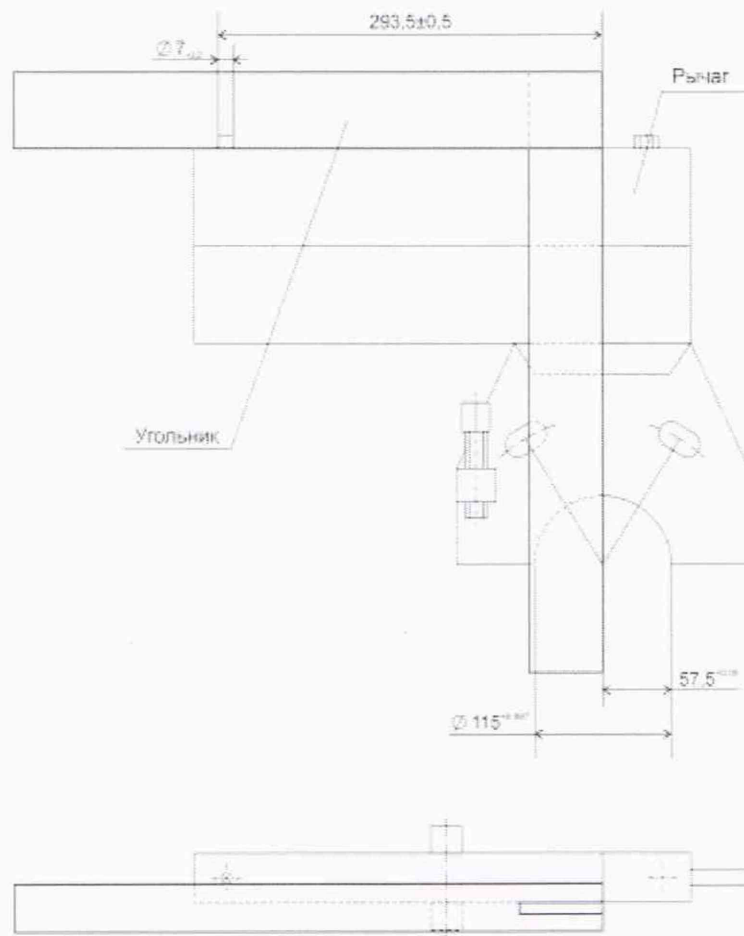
Чертеж рычага М 159.420.00.00
